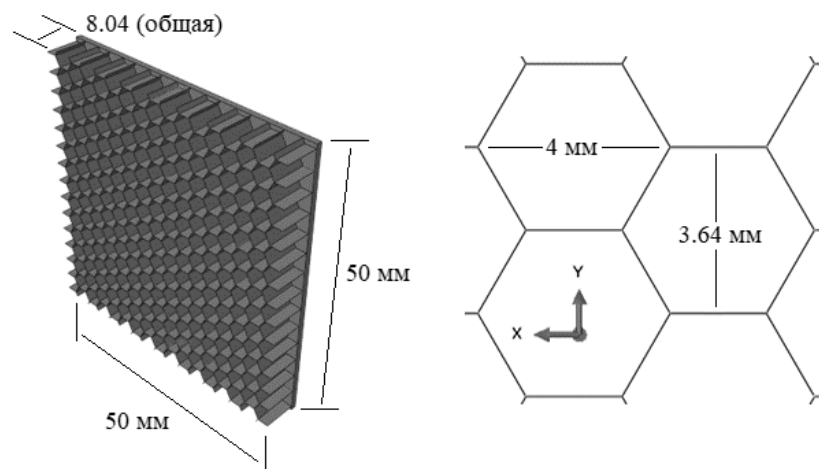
Трехслойный образец для испытаний по ASTM C364, верхняя обшивка для наглядности условно не показана.
